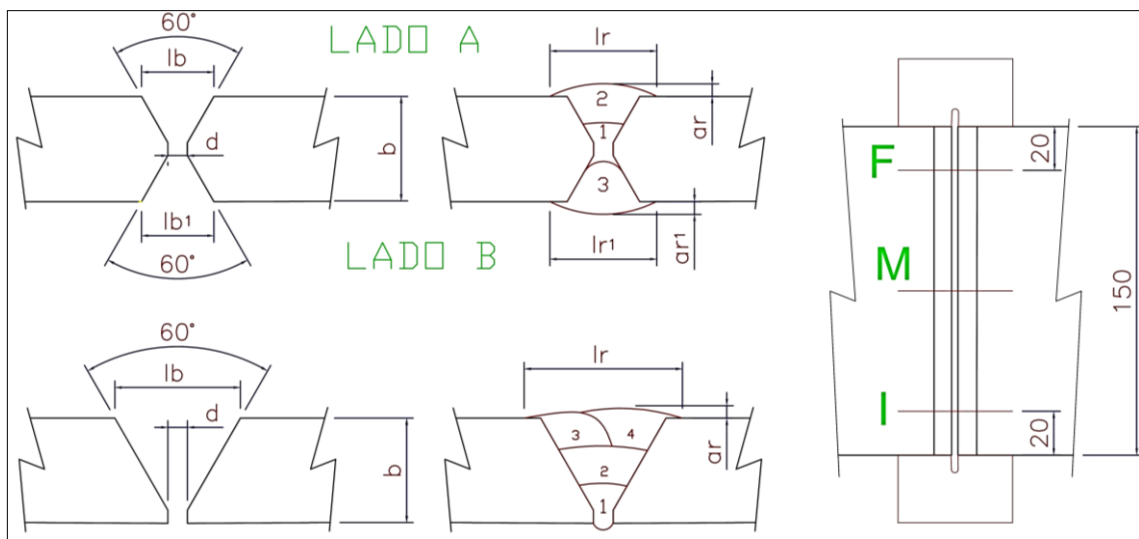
Croqui para controle dimensional dos biseis e das juntas soldadas.
